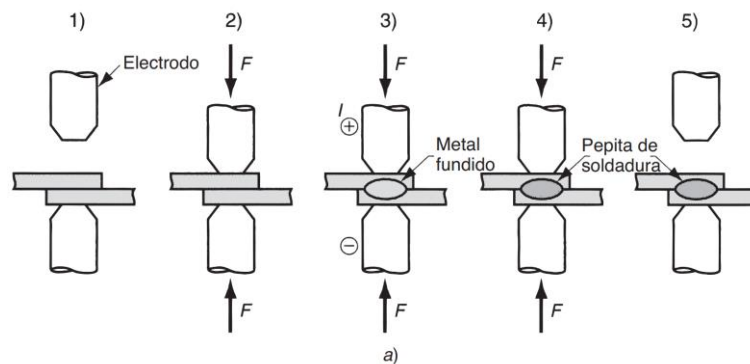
Secuencia de pasos del proceso de soldadura de puntos por resistencia [15]
